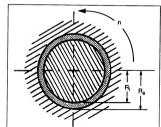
Поперечное сечение подшипника скольжения коленчатого вала с кольцевым зазором для смазки
